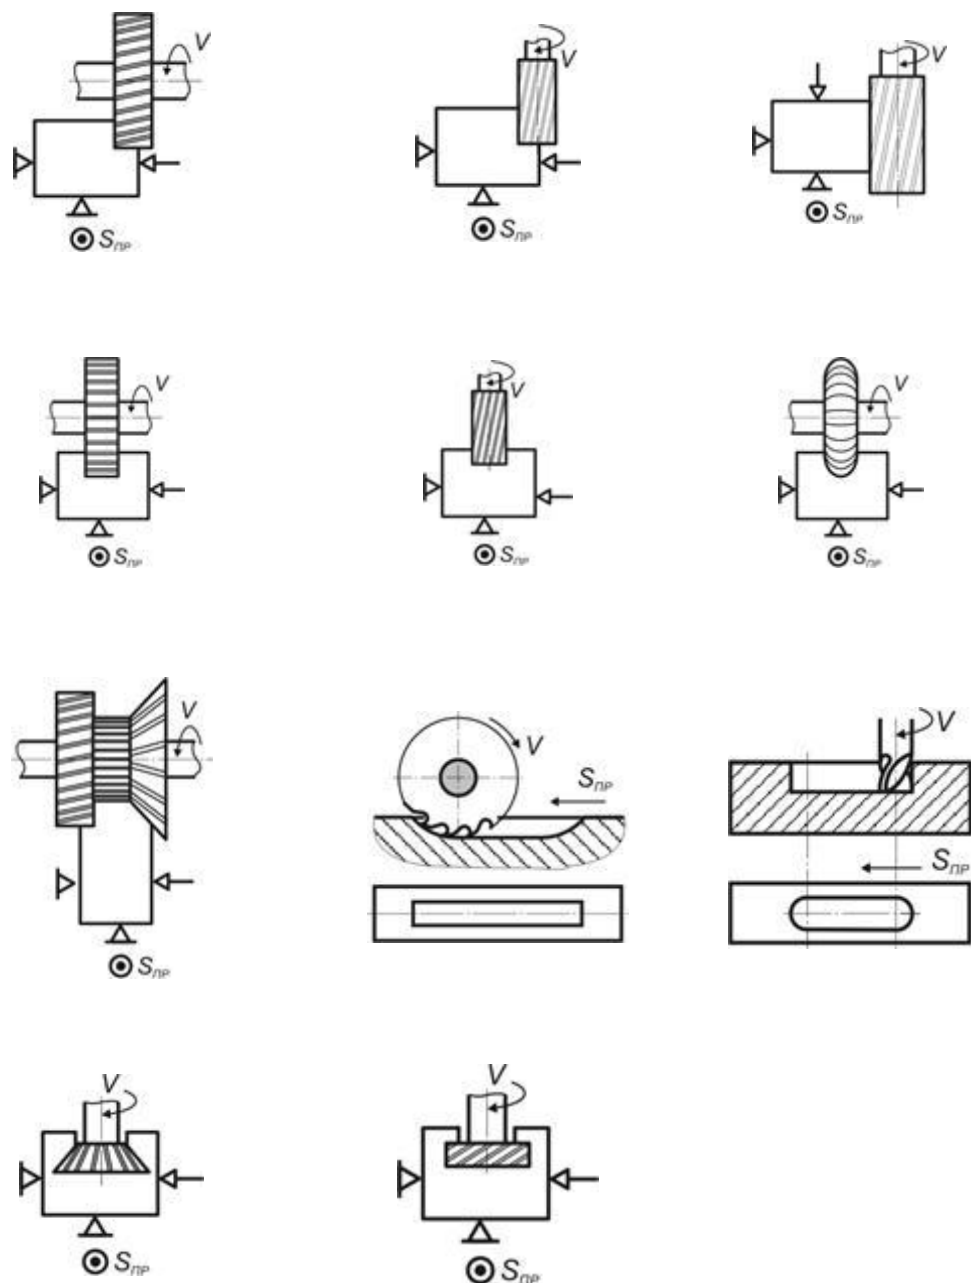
Схемы обработки поверхностей на вертикально- и горизонтально-фрезерных станках
